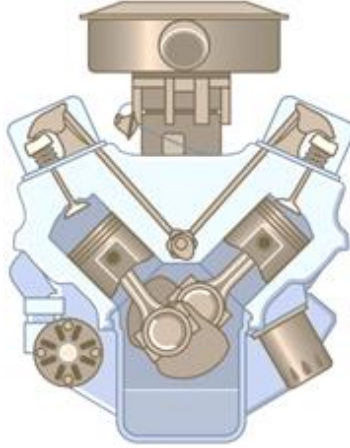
Motor de combustión interna que opera con gasolina [8].
